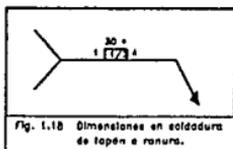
Dimensiones en soldadura de topón a ranura.
